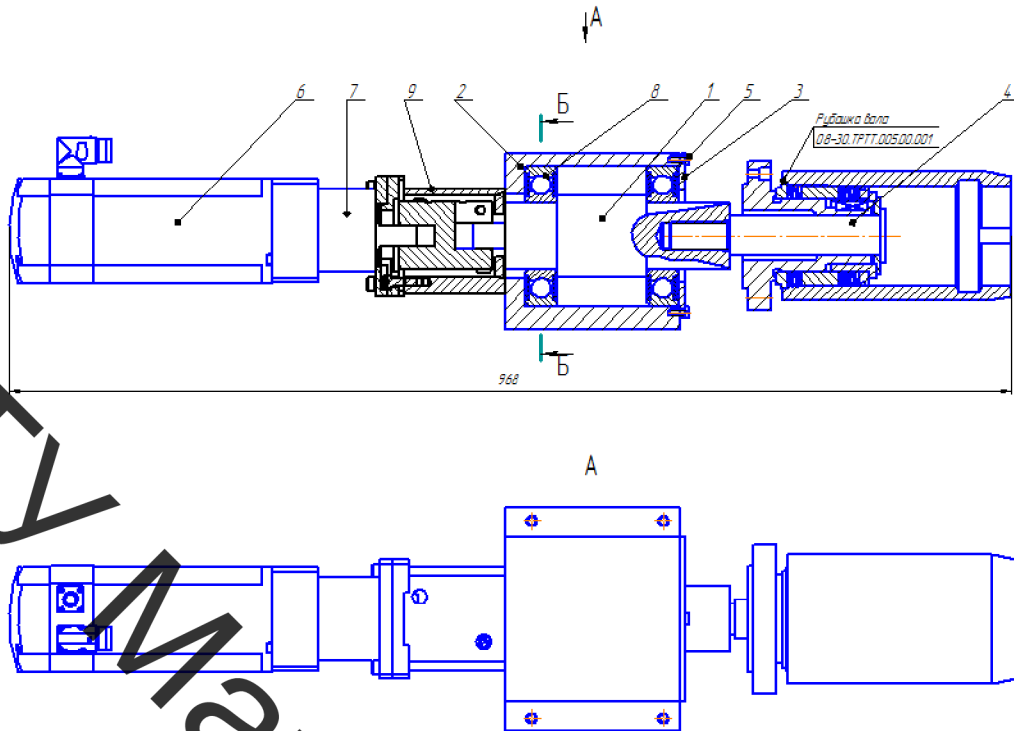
1 – вал, 2 – корпус, 3 – кришка, 4 – оправка, 5 – гвинт, 6 – сервомотор, 7 – редуктор; 8 – підшипник; 9 – осьовий набір;
